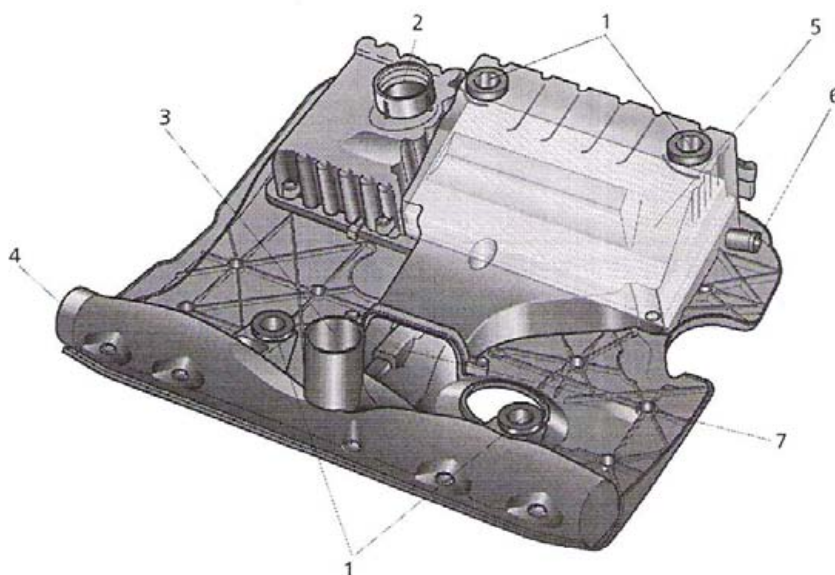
Šiesta montážna stanica pre montáž vrchného krytu motora so vzduchovým filtrom
